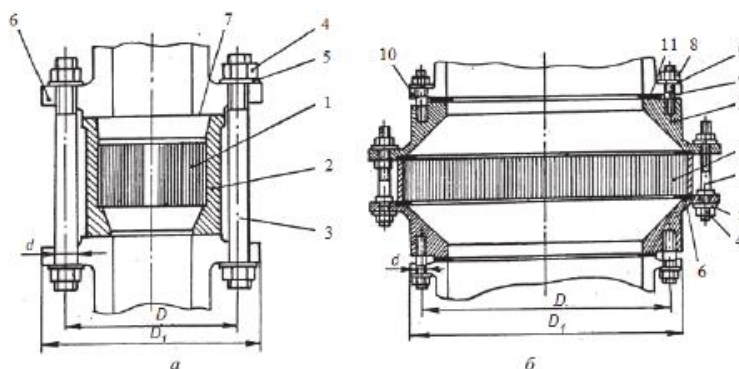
Полум'язапобіжники: а - ПП-50: 1 - полум'язапобіжний елемент; 2 - корпус; 3 - шпильки; 4 - гайки; 5 - шайби; 6 - фланці; 7 - прокладки; б - ПП-500: 1 - полум'язапобіжний елемент; 2 - корпус; 3, 7 - шпильки; 4, 8 - гайки; 5, 9 - шайби; 6 - прокладки; 10 - фланці; 11 – ущільнююча прокладка
